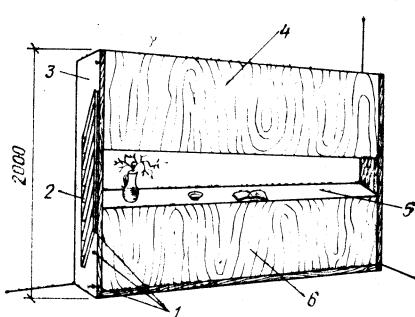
Общий вид мобильной, трансформирующейся двухъярусной детской кровати; 1 — ось-шарниры; 2 — складная лестница; 3 — стойка короба кровати; 4 — верхняя крышка; 5 — откидная доска; 6 — нижняя крышка
